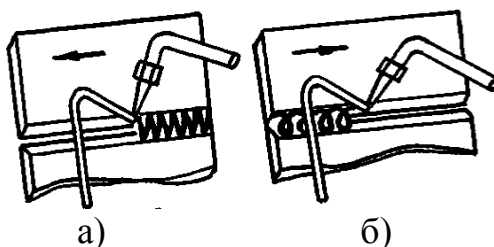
Способы сварки: а – левый; б – правый
